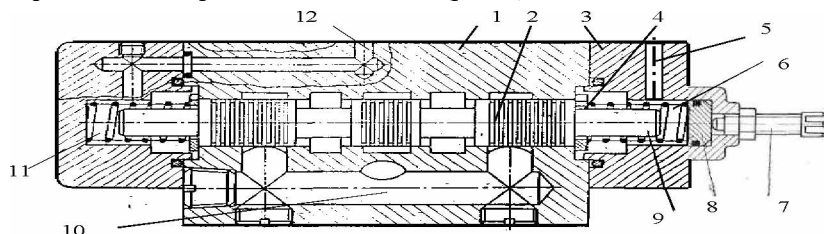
Конструктивная схема регулятора: 1-корпус; 2-плунжер; 3-крышка; 4-упор; 5,10,12- каналы; 6,11 - пружины; 7-винт регулировки поджатия пружин; 8- поршень; 9-шток.
